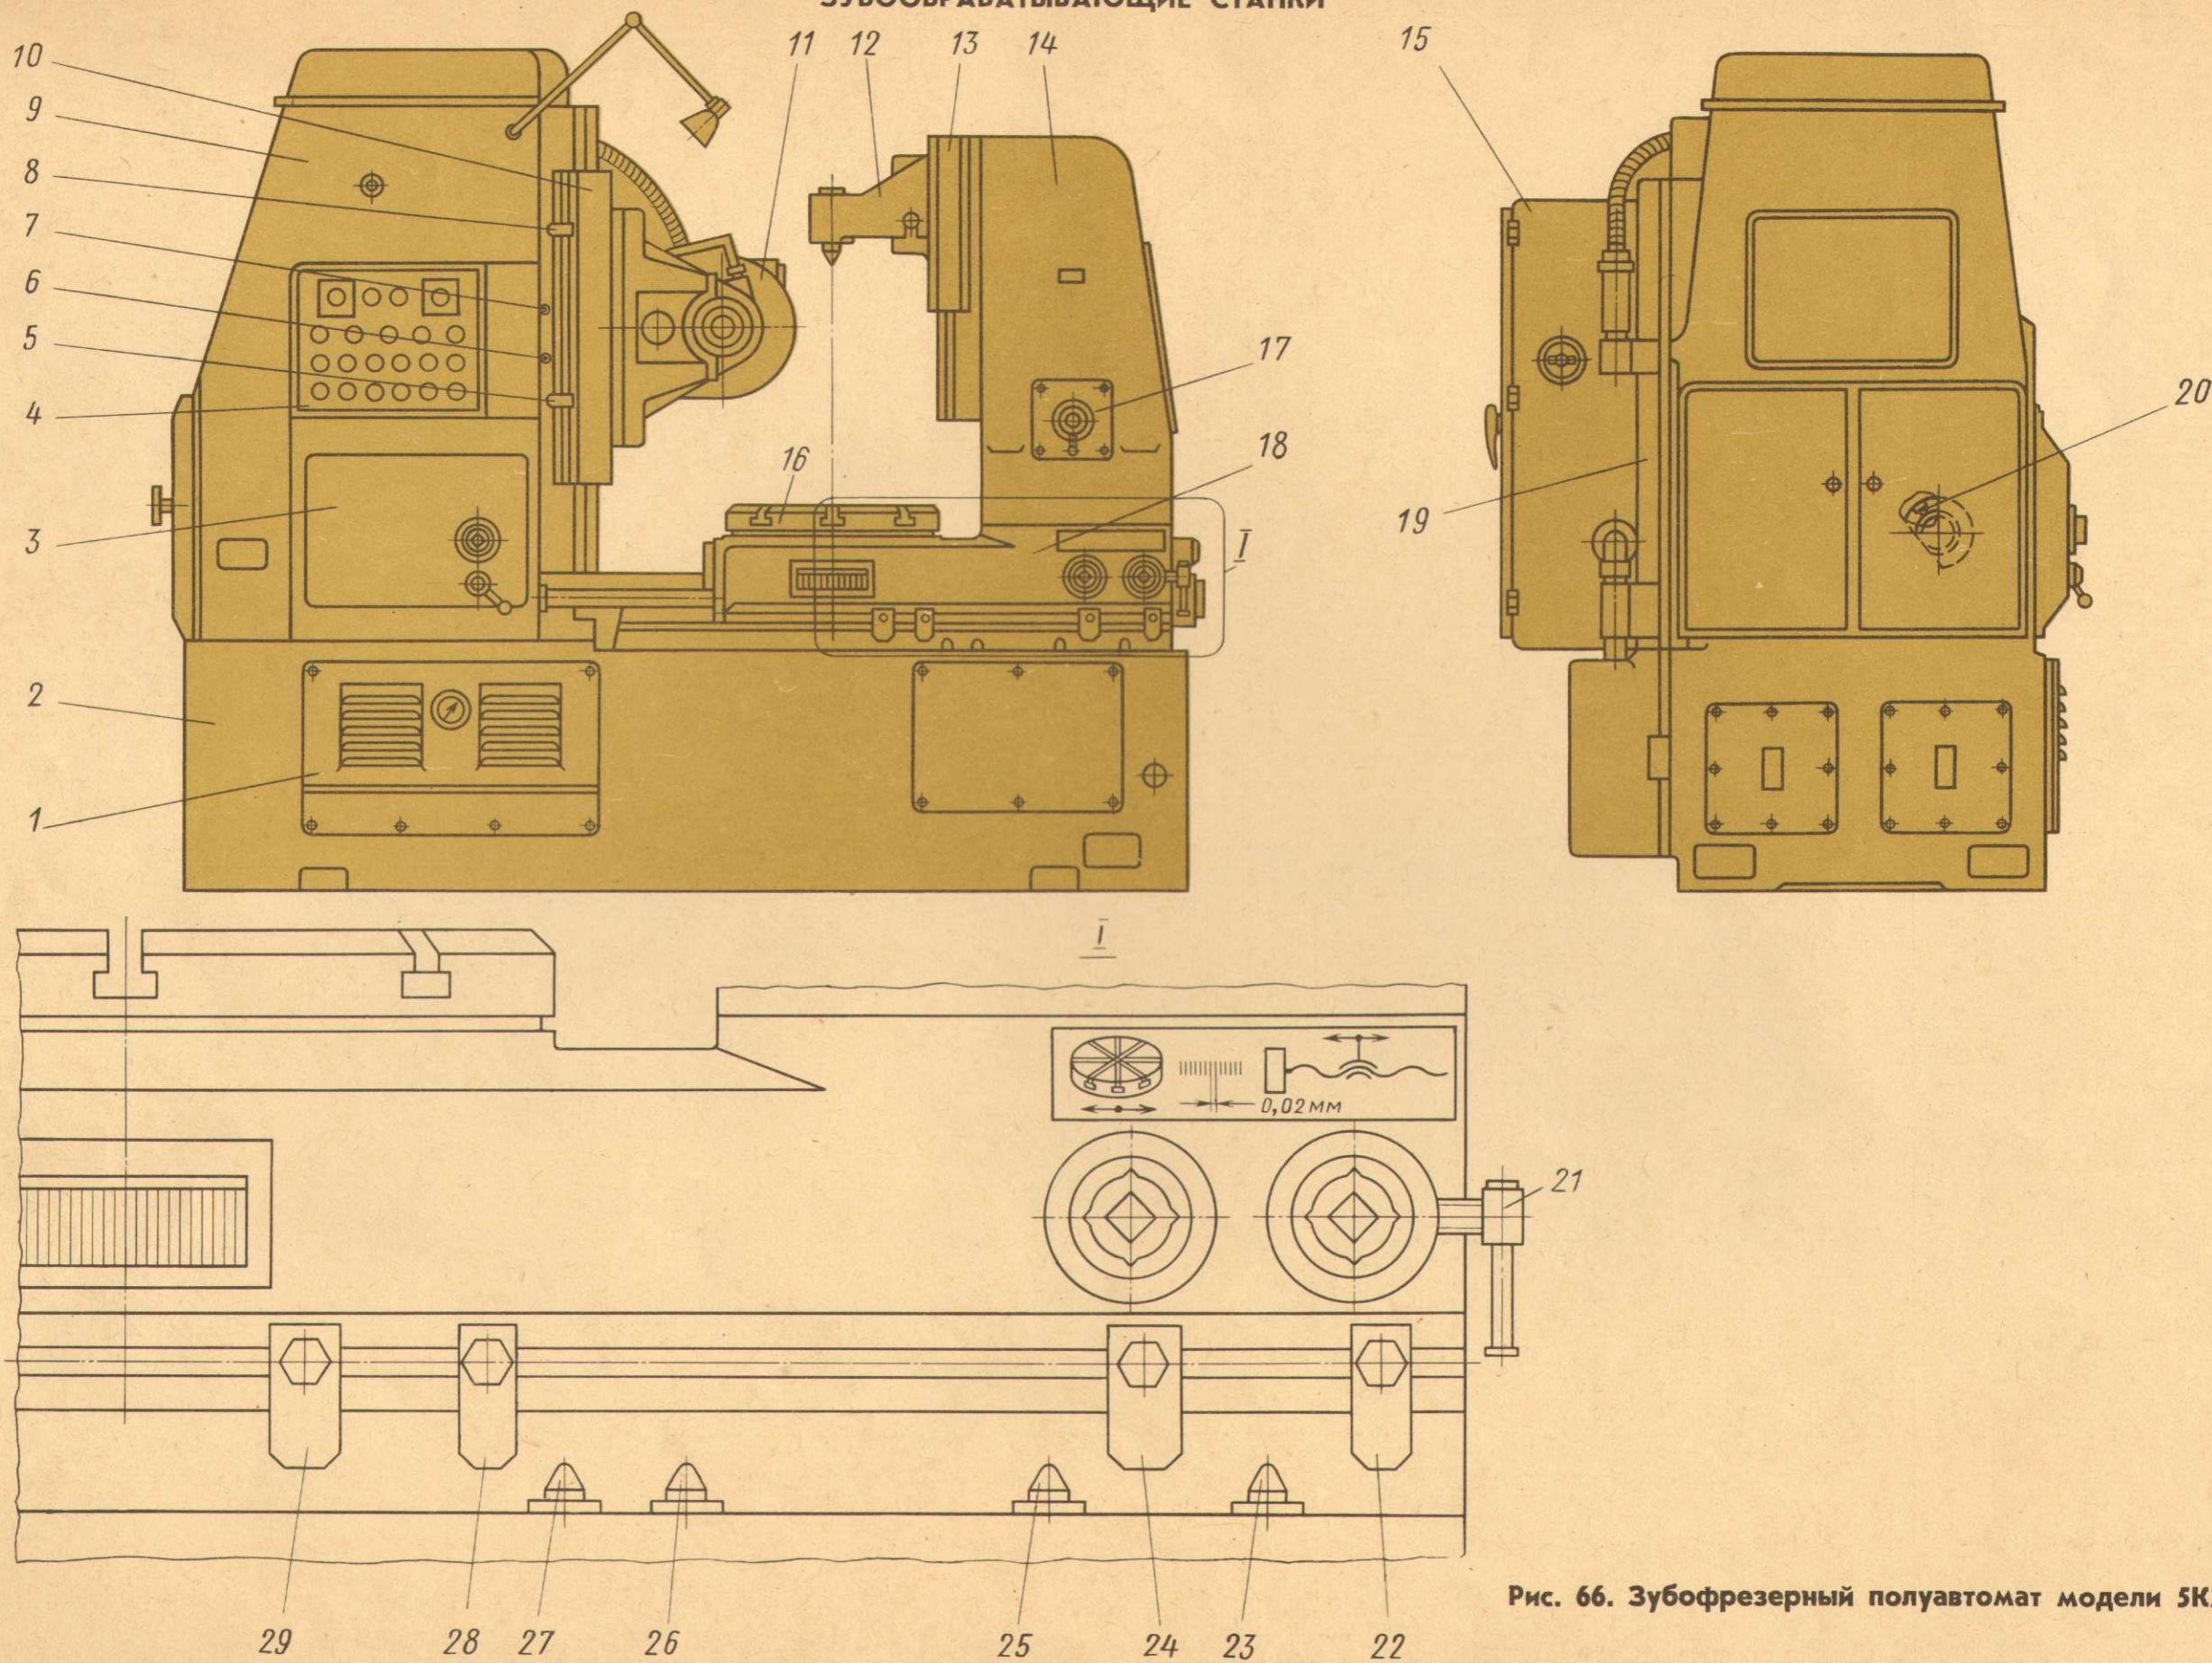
Зубофрезерный полуавтомат модели 5К32А
